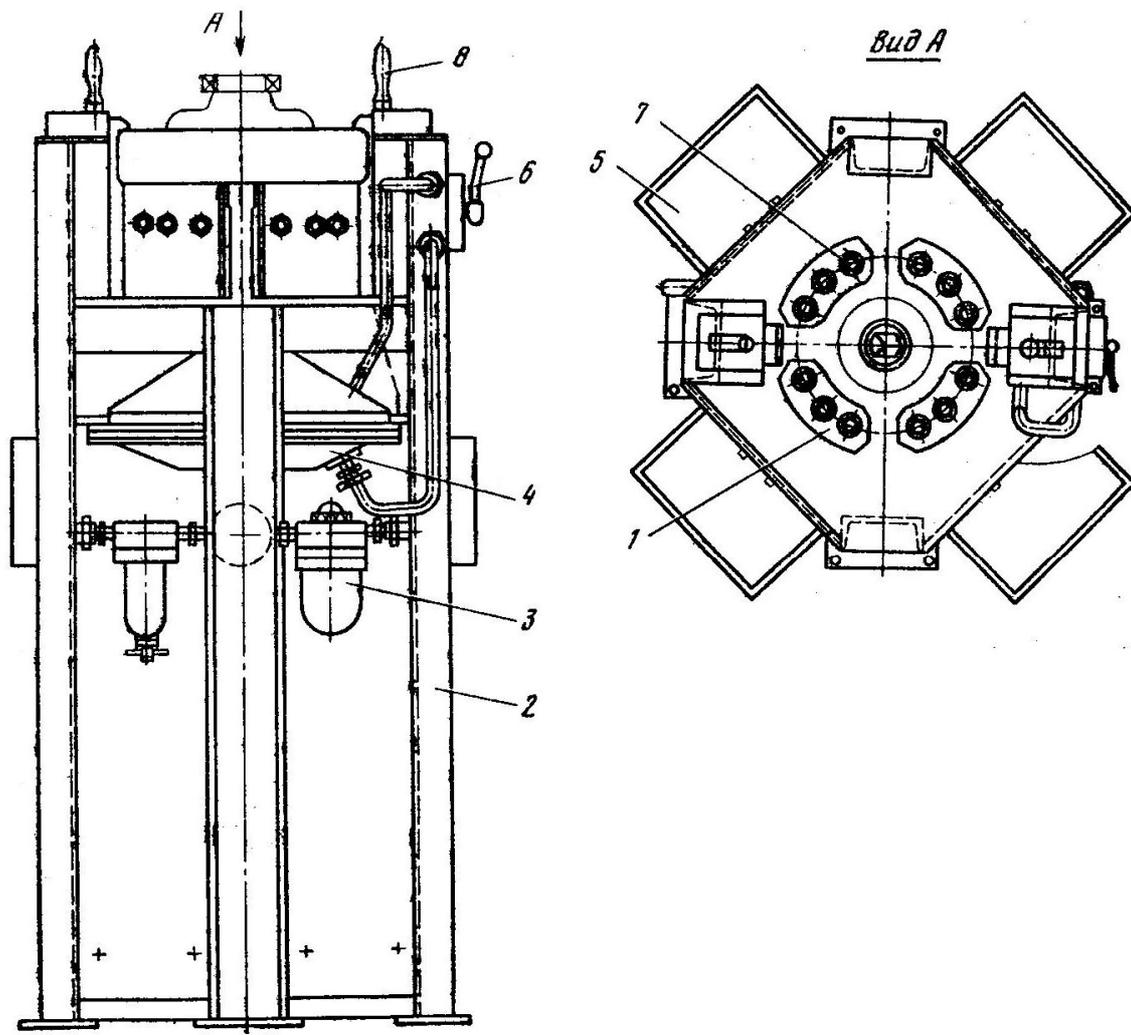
Приспособление для разборки дифференциала модель 70-7826-1525
